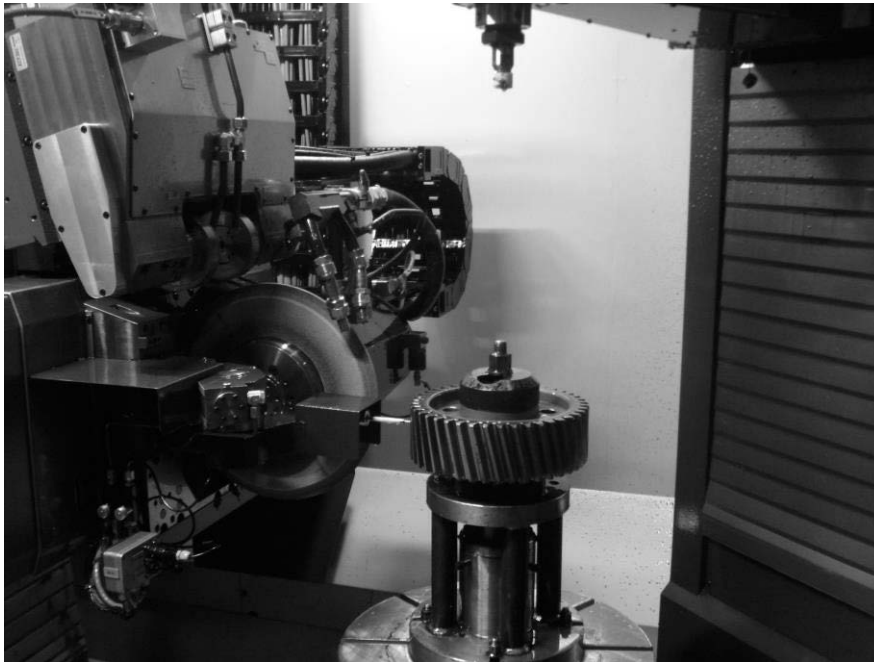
Обробка зубчастого колеса на зубошліфувальному верстаті моделі HOFLEER RAPID 1250
